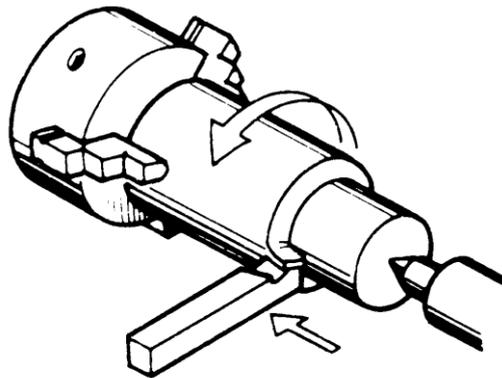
Обработка наружных цилиндрических поверхностей
